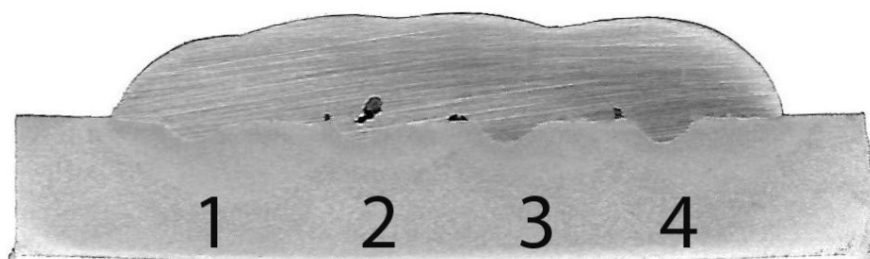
Macrografia da peça soldada pelo processo MIG-CW, velocidade de soldagem de 30 cm/min.
